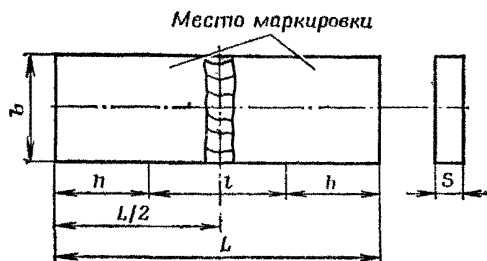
Форма и размеры плоского образца (разновидность), подготовленного для испытания сварного шва на разрыв
